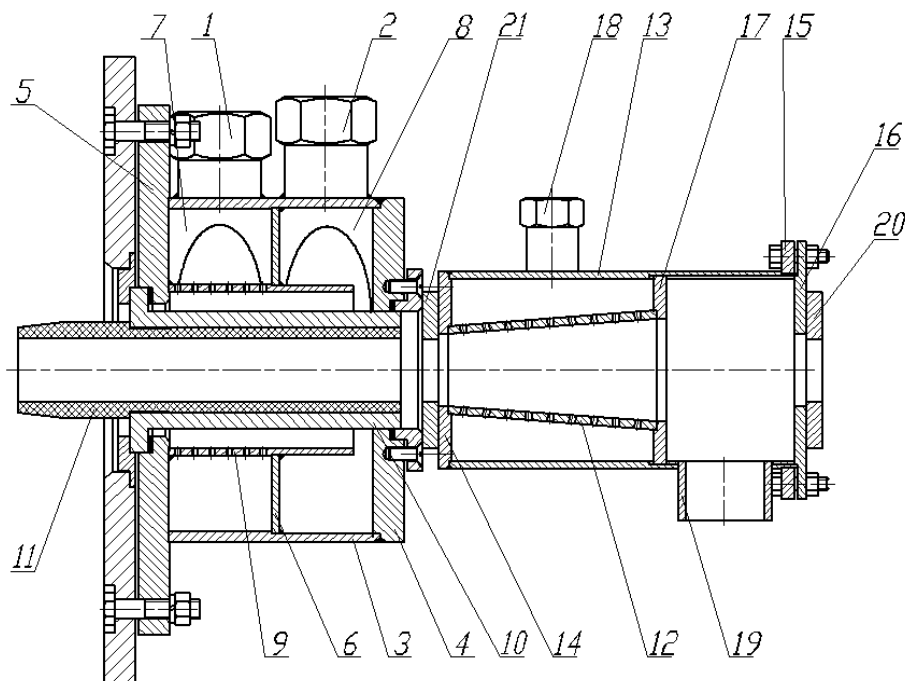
Схема струйного кристаллизатора с устройством затоплено-струйного вторичного охлаждения: 1 – подводящий патрубок; 2 – отводящий патрубок; 3 – корпус; 4, 5 – торцевые фланцы; 6 – перегородка; 7 – впускной коллектор; 8 – выпускной коллектор; 9 – экран; 10 – медная втулка; 11 – графитовая вставка; 12 – экран; 13 – кожух; 14 – левый фланец; 15 – правый фланец; 16 – крышка; 17 – заслонка; 18 – подводящий патрубок; 19 – отводящий патрубок; 20, 21 – гидрозаслонка
